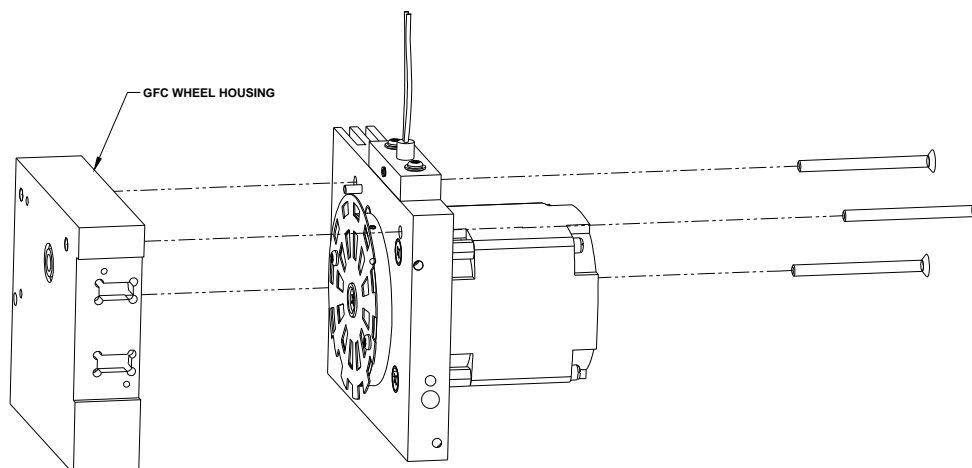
Entfernen des Gehäuses des GFC Rades
